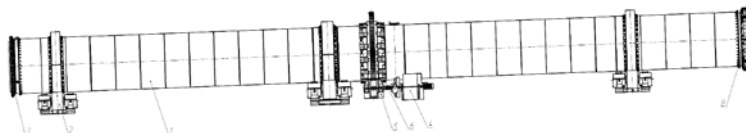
Вращающаяся печь  $\varnothing 4 \times 60$  м: 1 – корпус печи; 2 – роликоопора 400; 3 – роликоопора 450; 4 – привод; 5 – установка подвенцово́й шестерни; 6 – шестерня венцовая; 7 - уплотнение горячего конца; 8 – уплотнение холодного конца; 9 – ролик упорный
